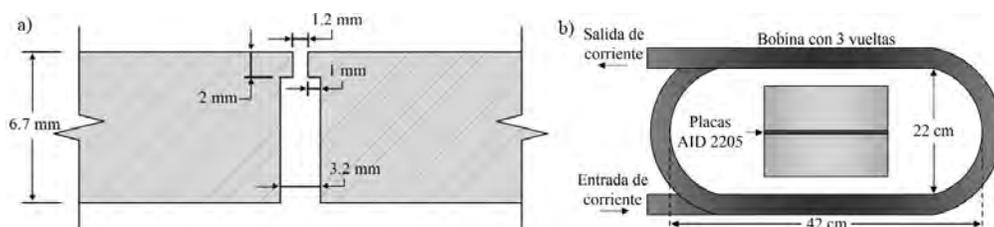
a) Preparación de las juntas soldadas para AEIM, b) dimensiones de bobina en el arreglo experimental.
